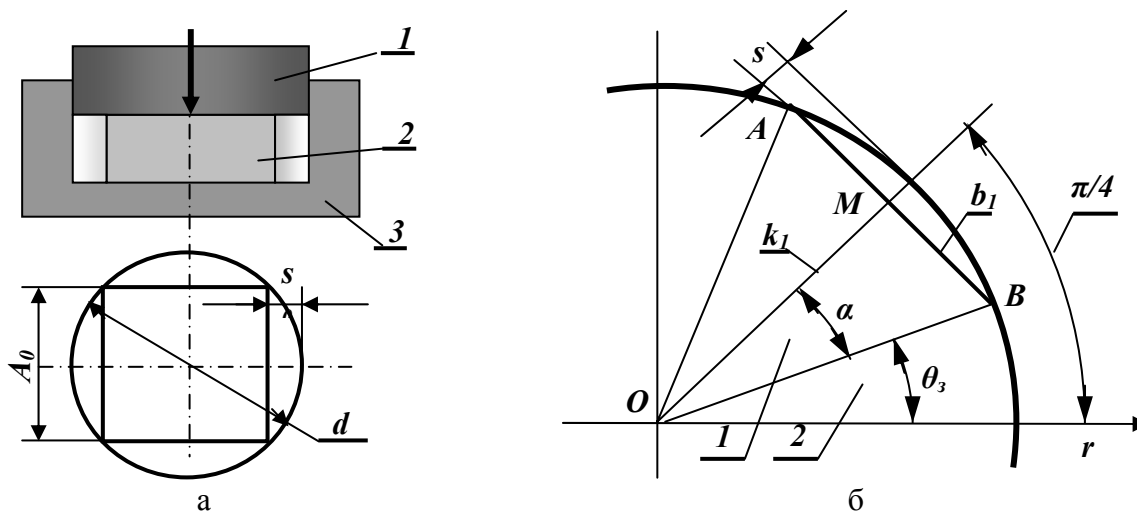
Схема осадки квадратной заготовки в цилиндрической матрице (а): 1 – пуансон; 2 – заготовка; 3 – матрица; разбивка заготовки на области (б)
